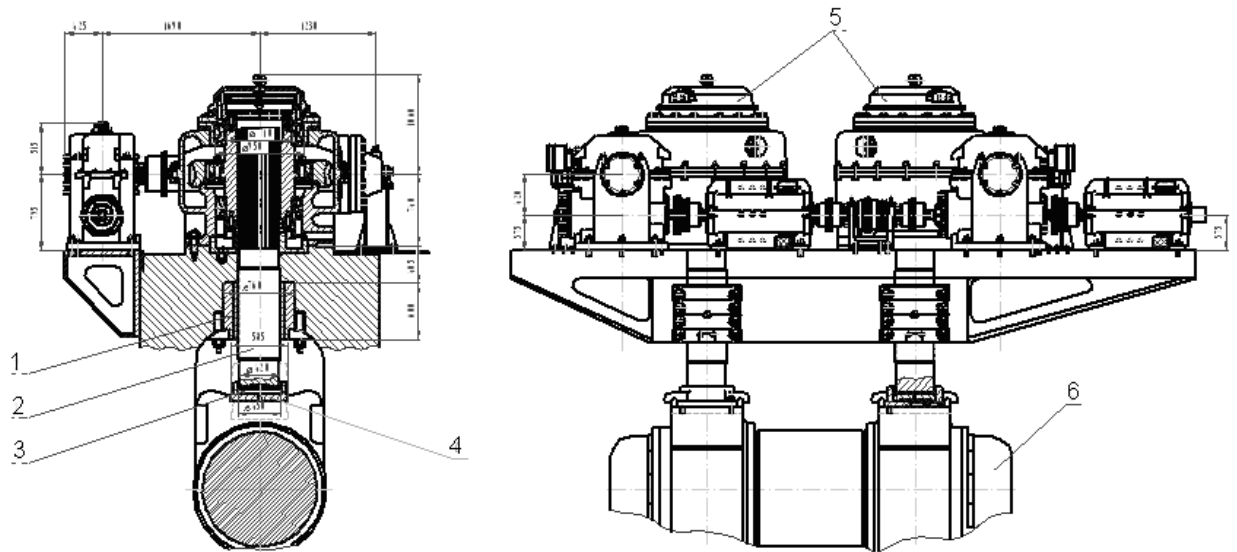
Натискний пристрій реверсивного стану 1200: 1 - гайка натискного гвинта; 2 – натискний гвинт; 3 – підп'ятник; 4 – стакан; 5 – редуктор; 6 – опорний валок
